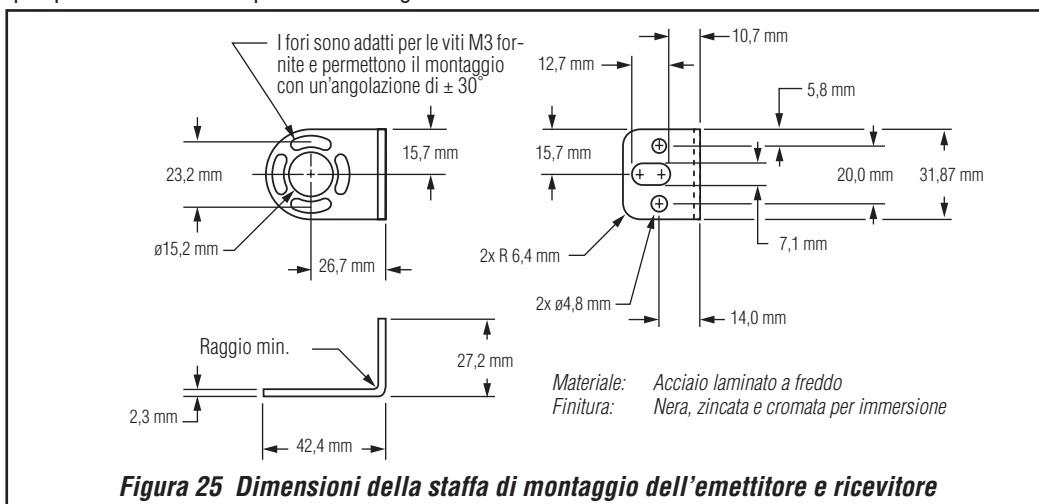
Dimensioni della staffa di montaggio dell'emettitore e ricevitore
